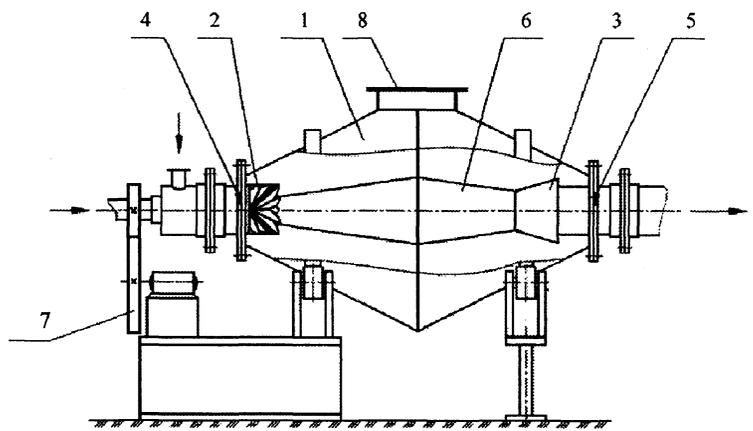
Ротационное двухкорпусное сушило: 1 – корпус сушила; 2 – завихритель; 3 – сепаратор; 4, 5 – уплотнители; 6 – корпус разделителя потоков газов; 7 – привод; 8 – загрузочное окно (пат. РБ № 1732)
